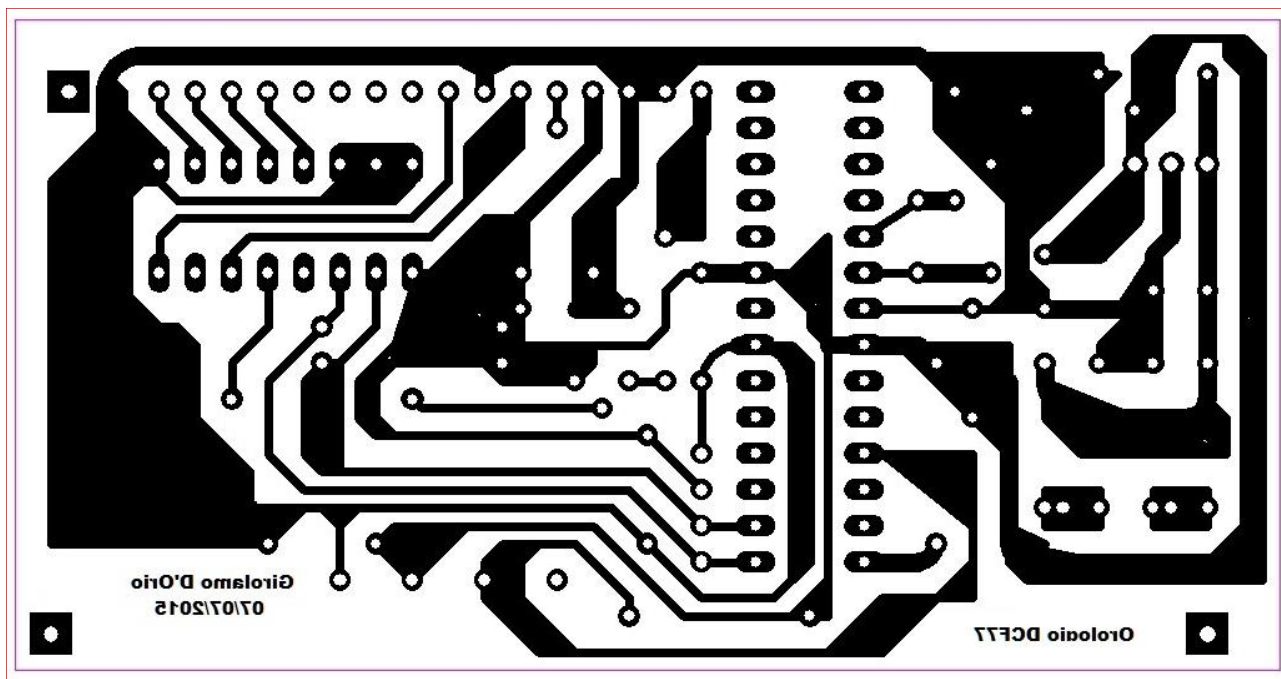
Il master del PCB (88,6 x 45,6 mm)
